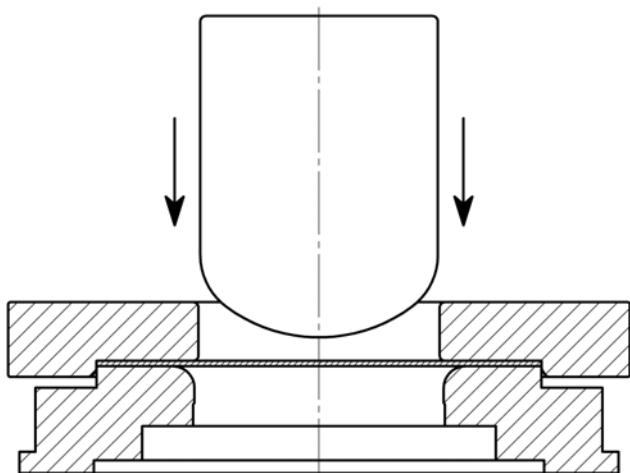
Схема расположения инструмента и заготовки для операции свертки
